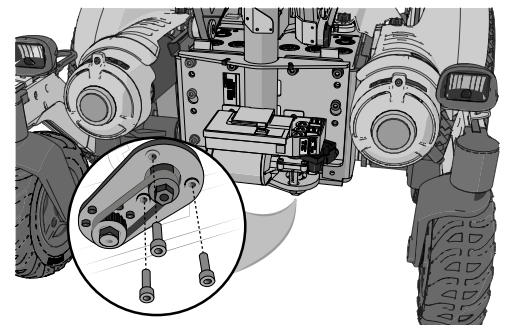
Der Motor ist mit drei Schrauben befestigt.
